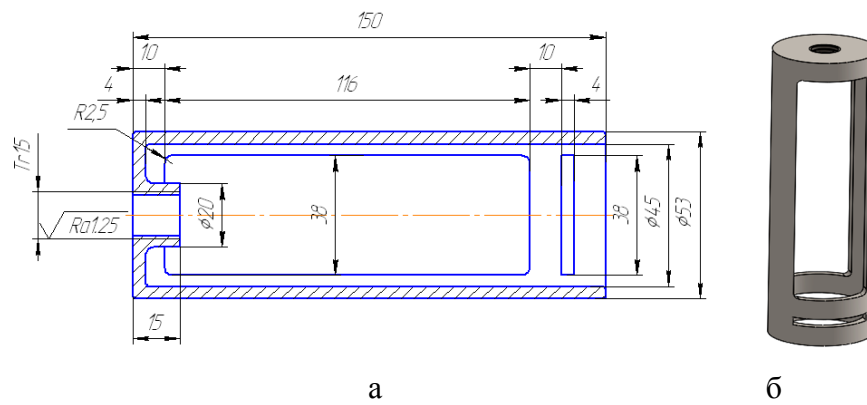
Креслення (а) й 3D-модель корпусу (б).
